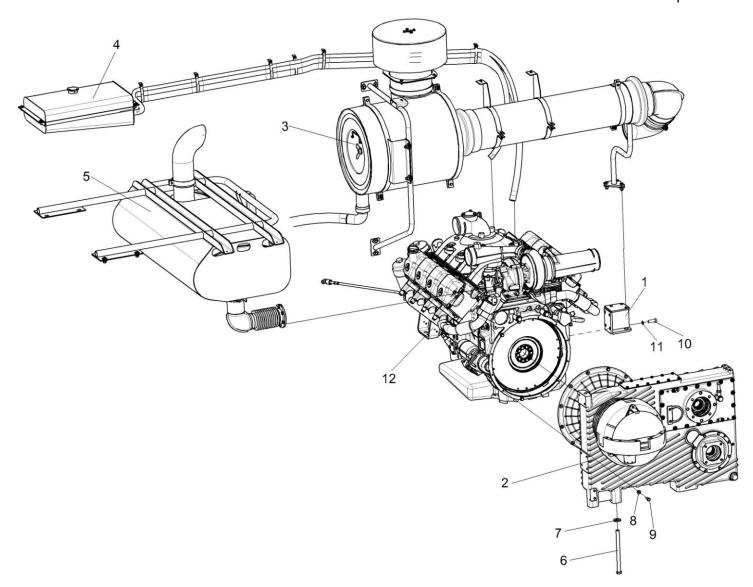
Установка двигателя OM502LA KBK 0150000 (установка главного привода, воздухоочистителя, бачка расширительного и глушителя)
